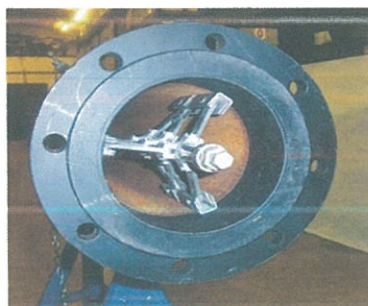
Приспособление для напасовки фланца с центровкой по внутреннему диаметру трубы
